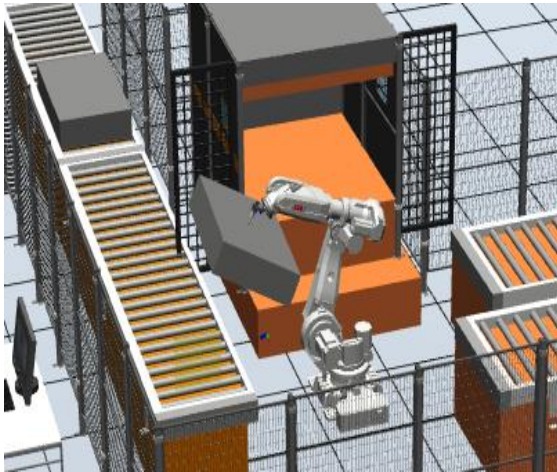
Agarre de pieza sin mecanizar en la primera etapa.
